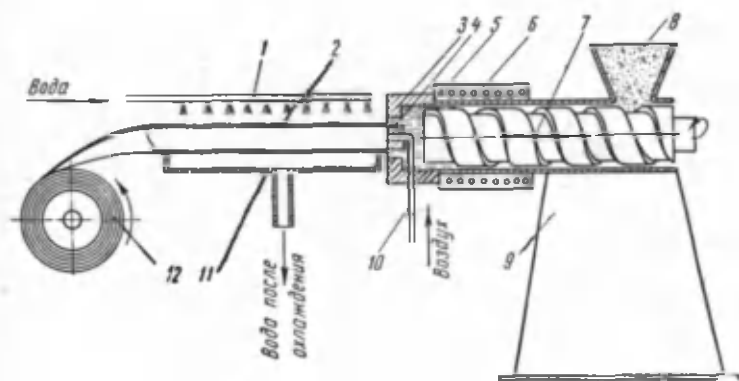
Схема работы шприц-пресса для изготовления полихлорвиниловой трубки:
